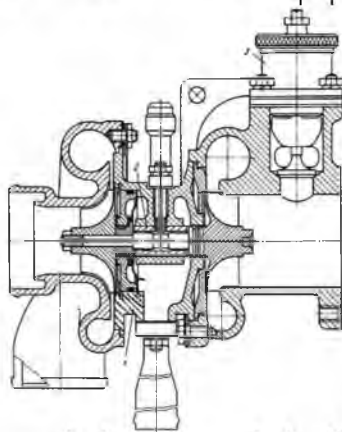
Компресорне устаткування типорозміру ТКР 5,5
